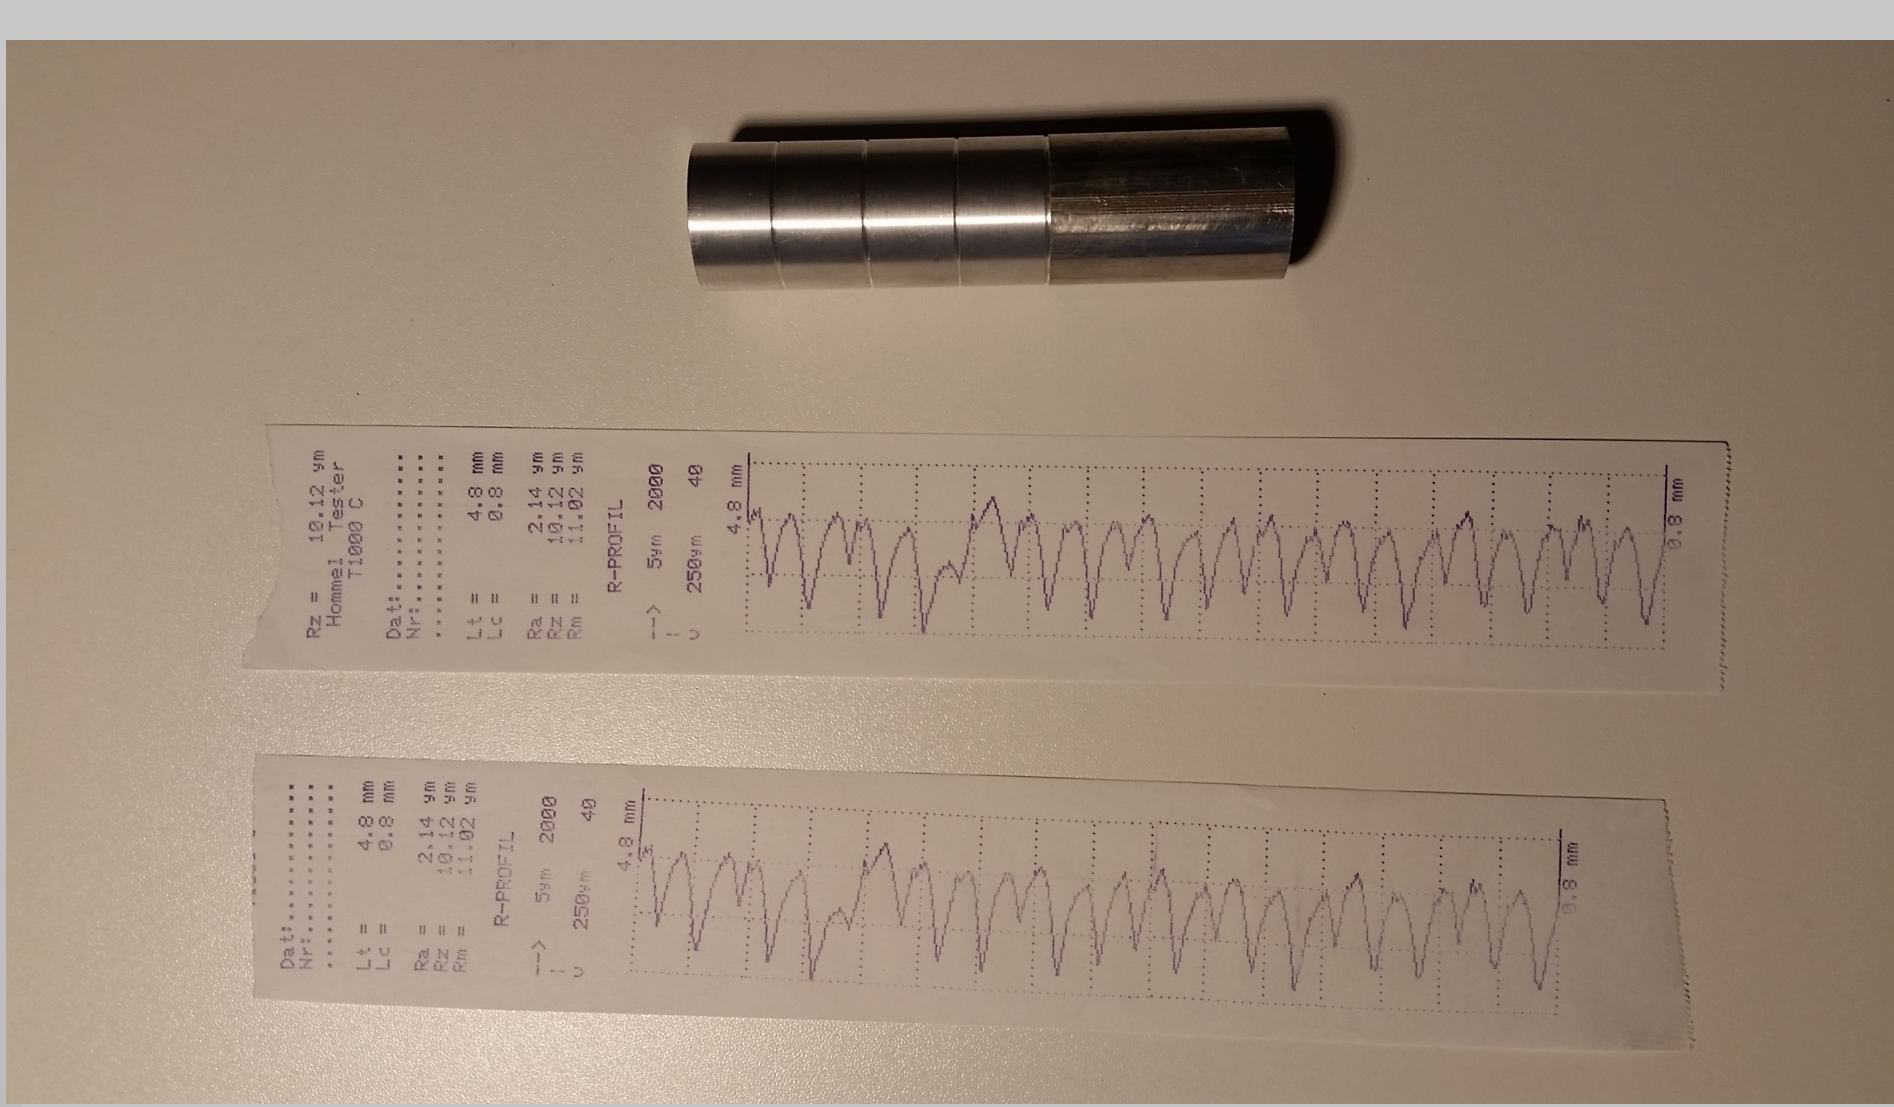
Werkstückprobe und Ausdruck des Tastschnittgeräts
